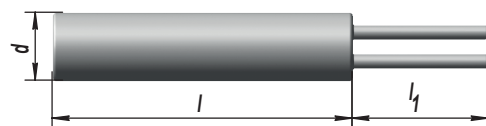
Материал корпуса-нержавеющая сталь, латунь
